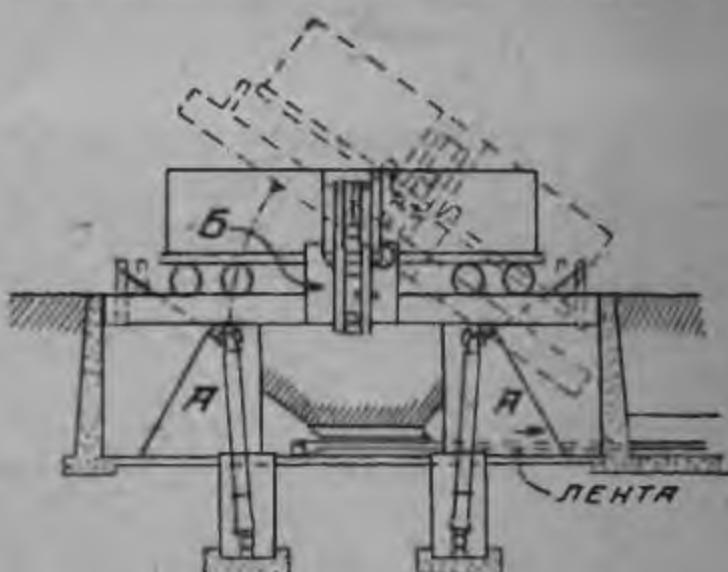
Тип торцово-бокового вагоноопрокидывателя для выгрузки зерна.
